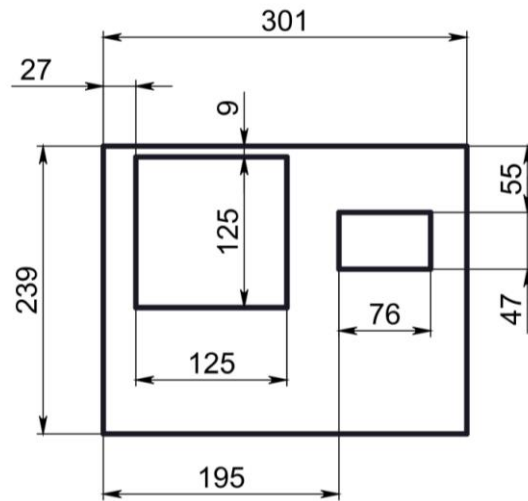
Габаритные, установочные и присоединительные размеры
